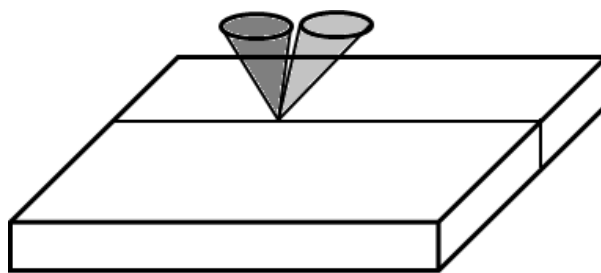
Схема двухлучевой суперпозиционной сварки
